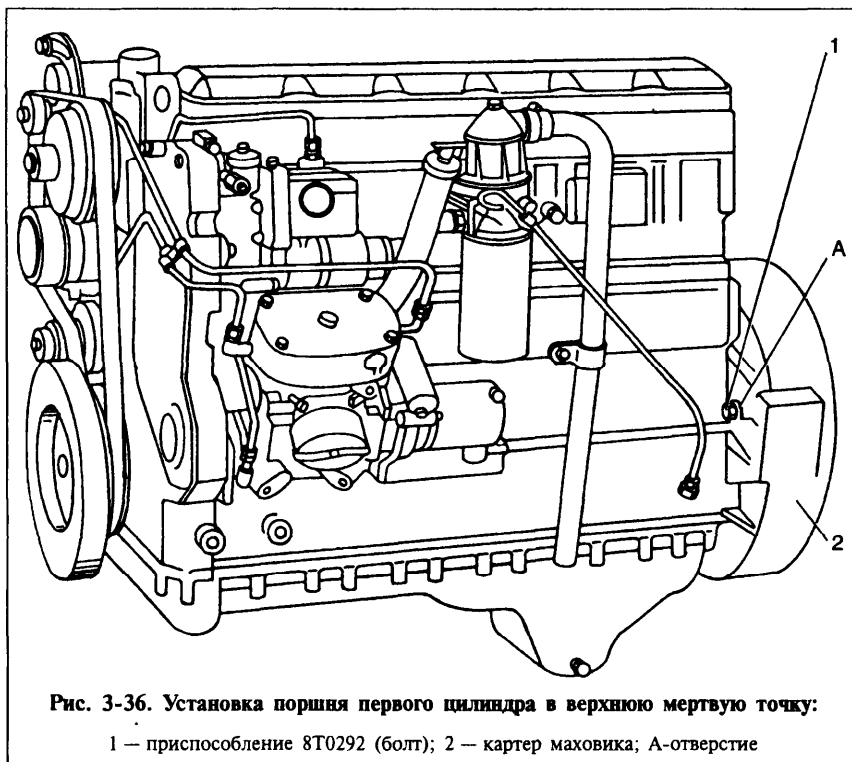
Установка поршня первого цилиндра в верхнюю мертвую точку:
